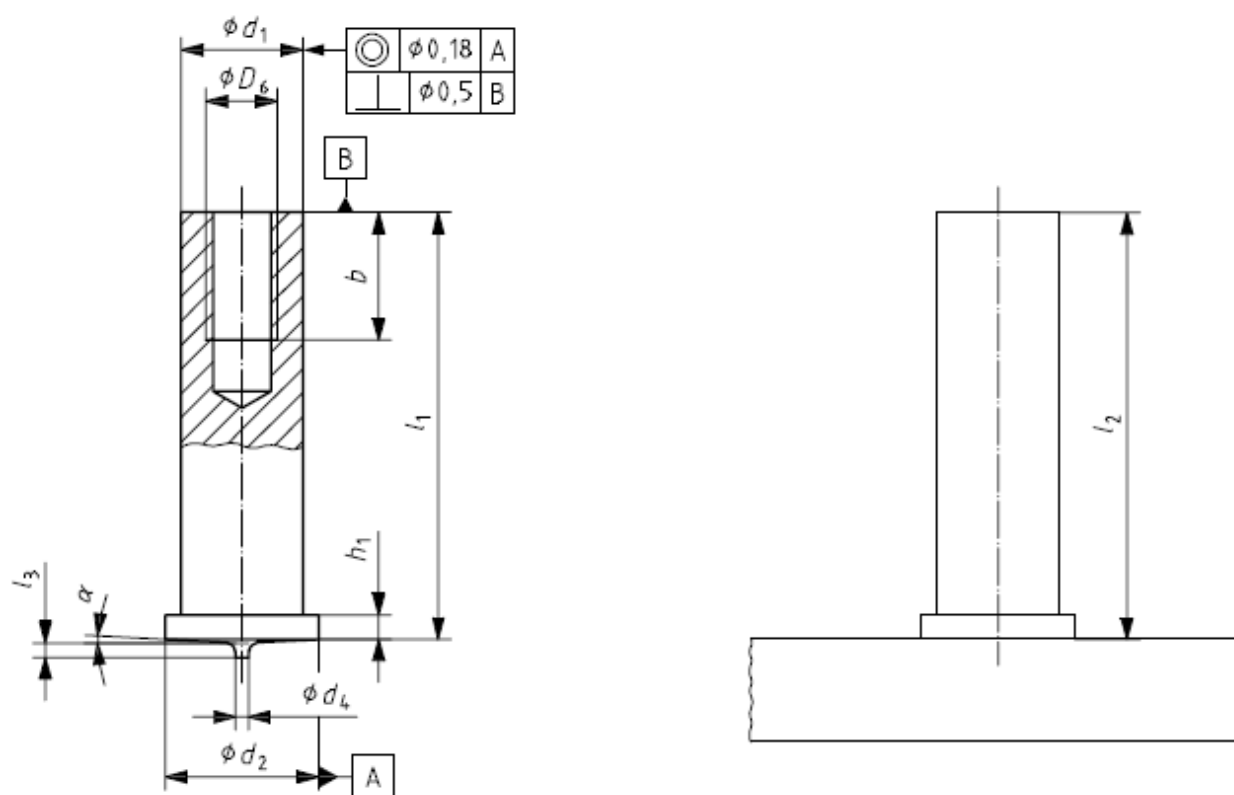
Шпилька с внутренней резьбой (IT)
